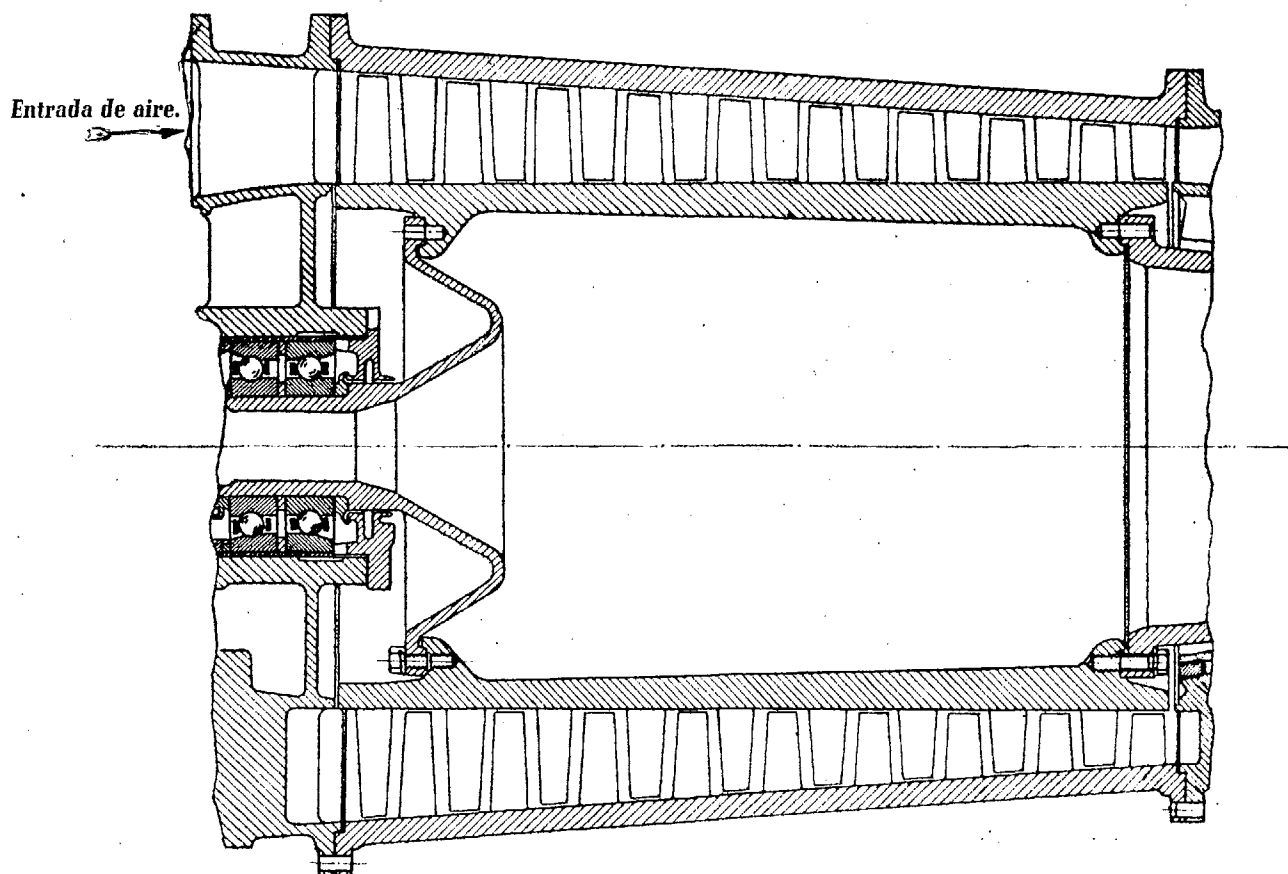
Esquema de un compresor axial de construcción en tambor (Ref. 3).
